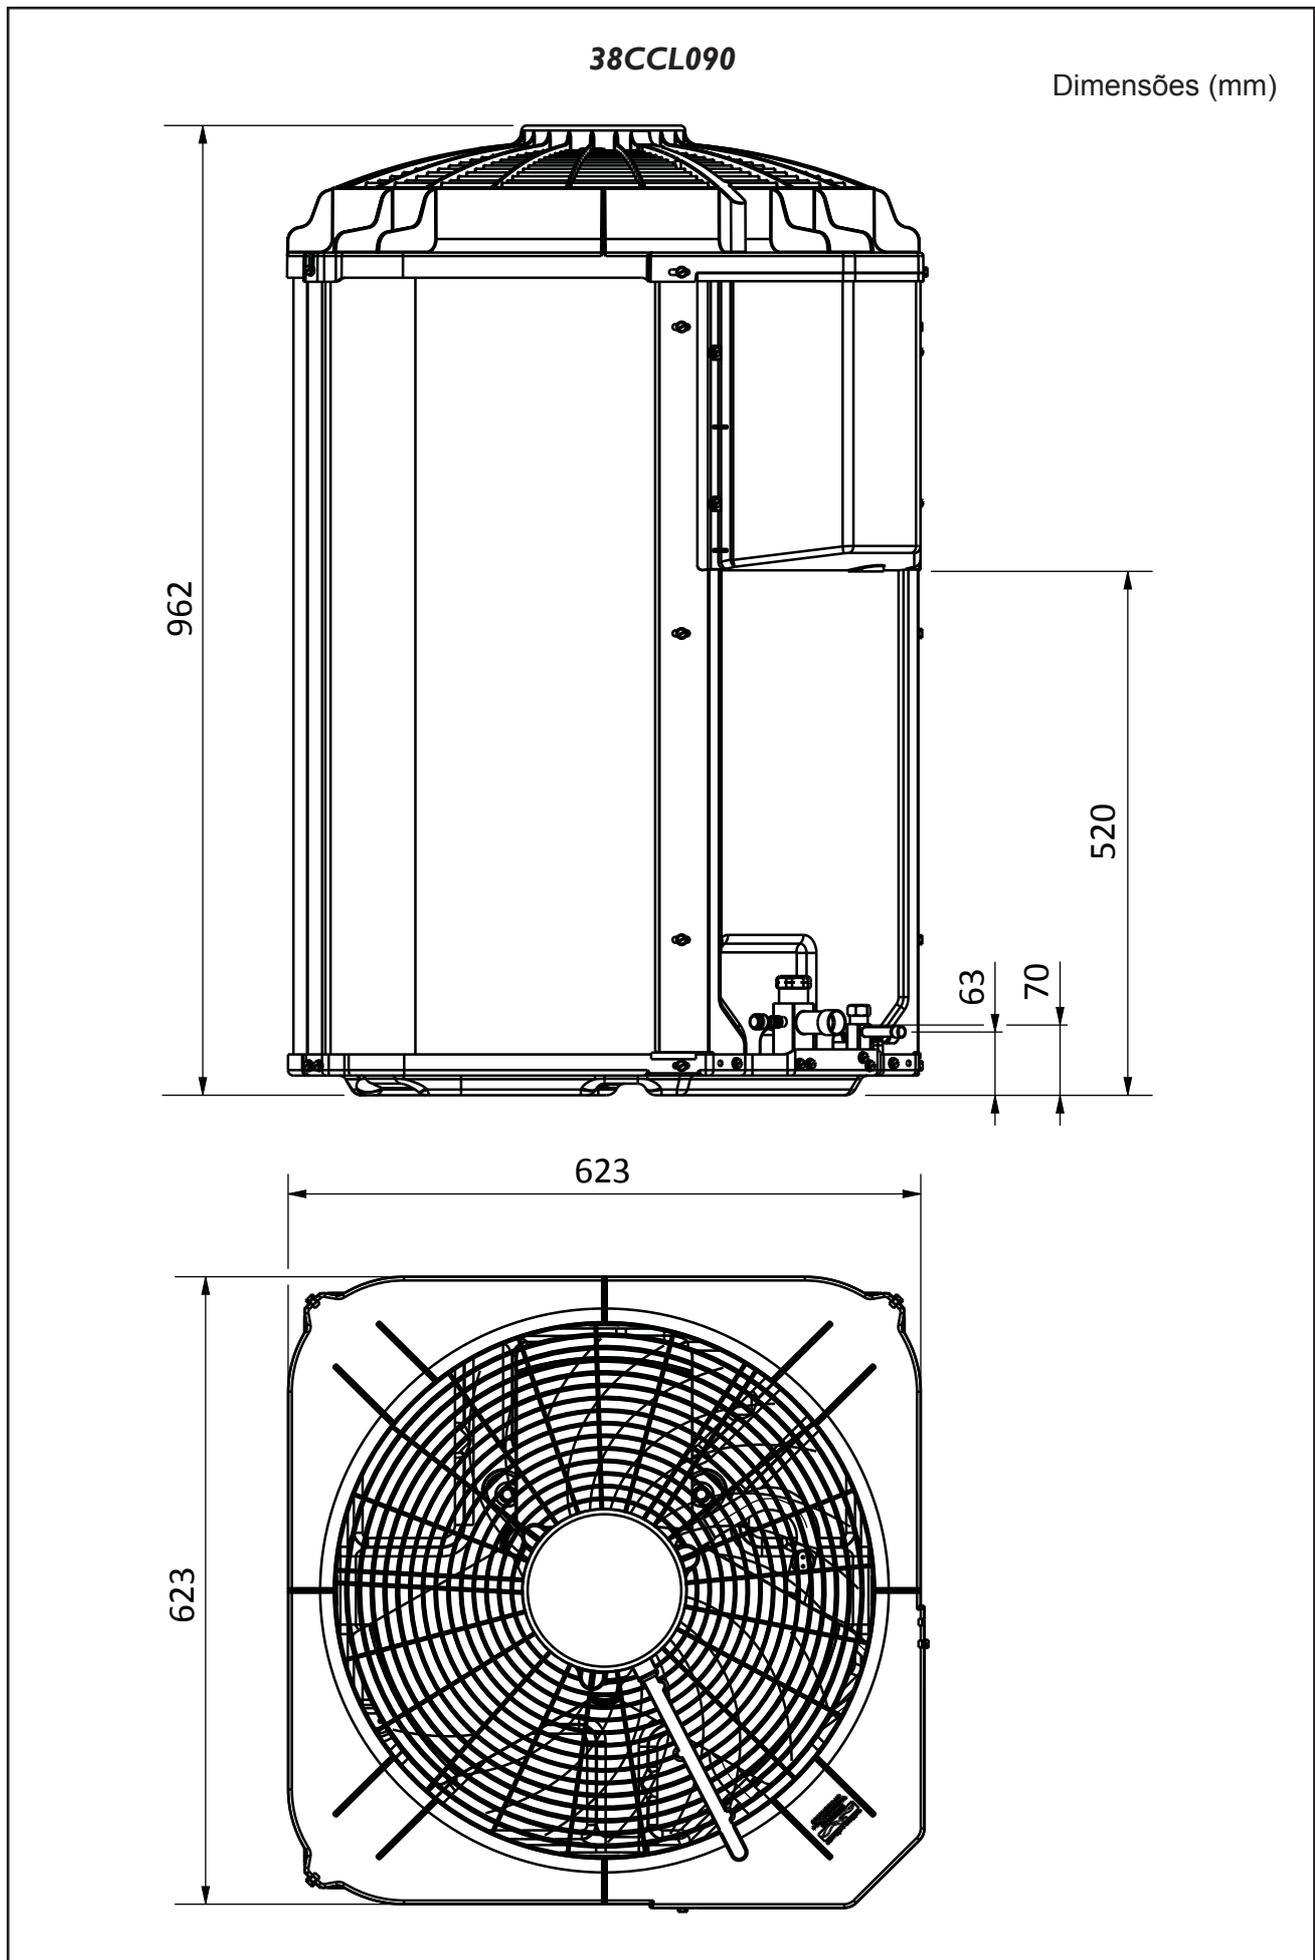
DIMENSIONAL UNIDADES CONDENSADORAS
